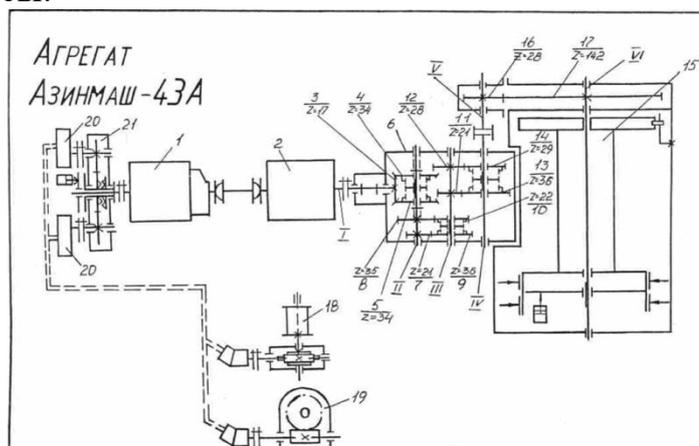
Кинематическая схема агрегата Азинмаш 43А
